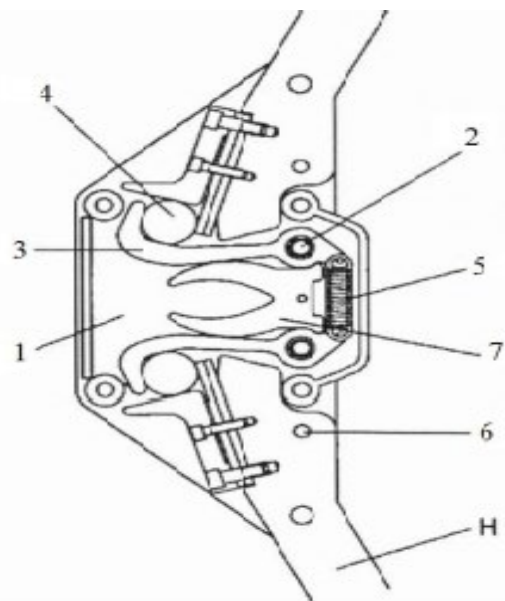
Шарнірний поворотний плуг напівавтоматичний запобіжний замок фірми Lemken [9].
